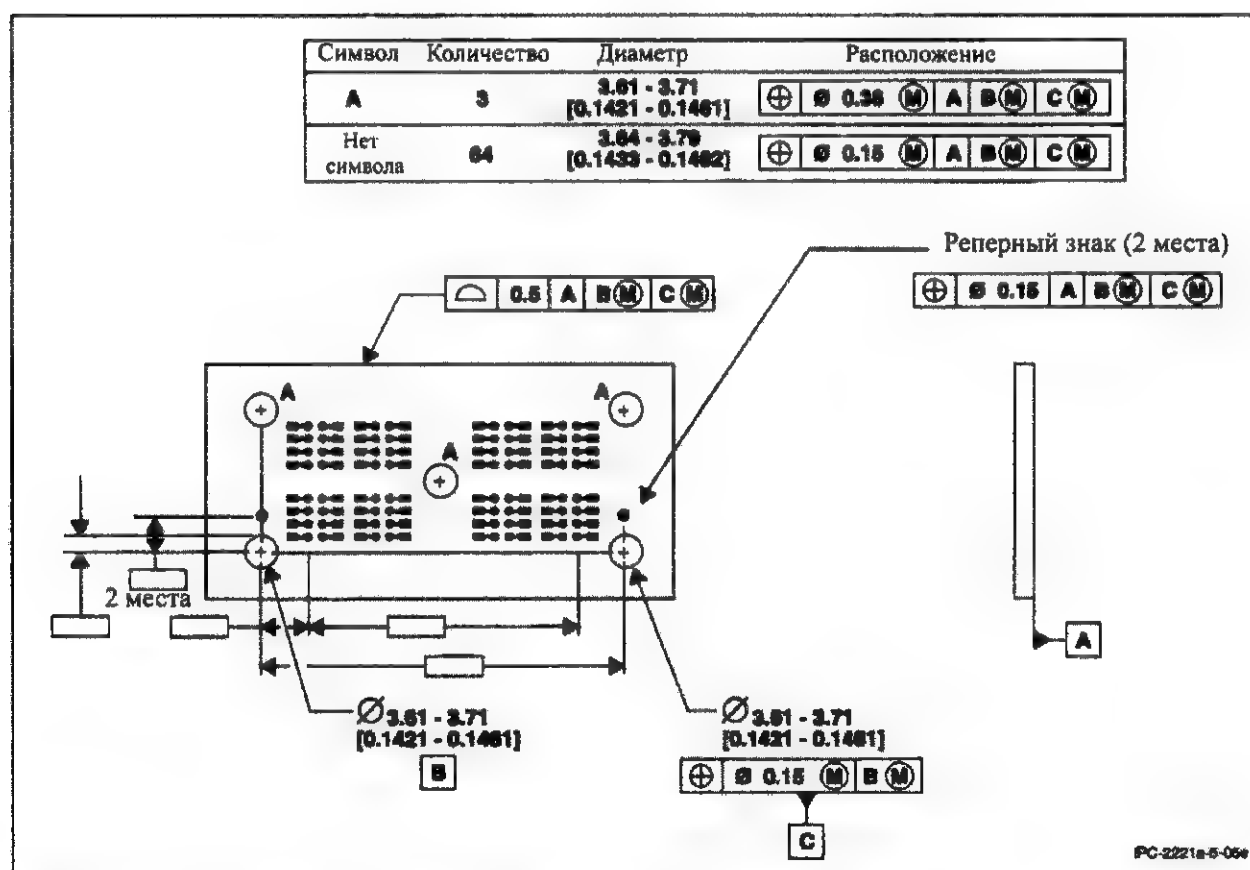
E Пример простановки на чертеже печатной платы размеров и допуска, мм.
